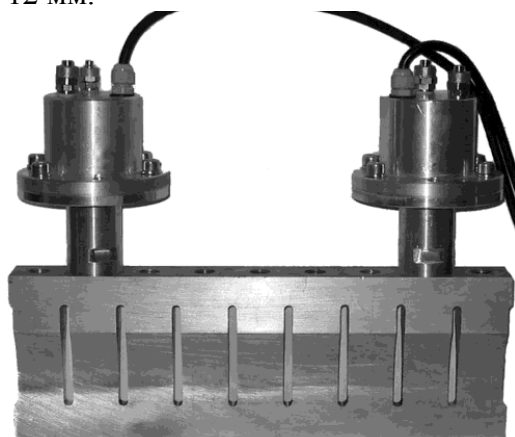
Ультразвуковая колебательная система для обеспечения сварного шва длиной 360 мм
